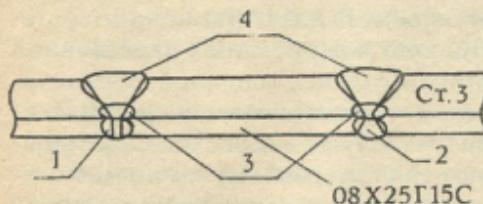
Сварка полос биметалла: 1 - корень V-образной канавки, сварка АДС; 2 - корень шва X-образной канавки, сварка ЭДС; 3 - переходные зоны, сварка ЭДС (эл. ОЗЛ-17У); 4 - основной металл Ст. 3, сварка ЭДС (эл. УОНИ-13/55)
